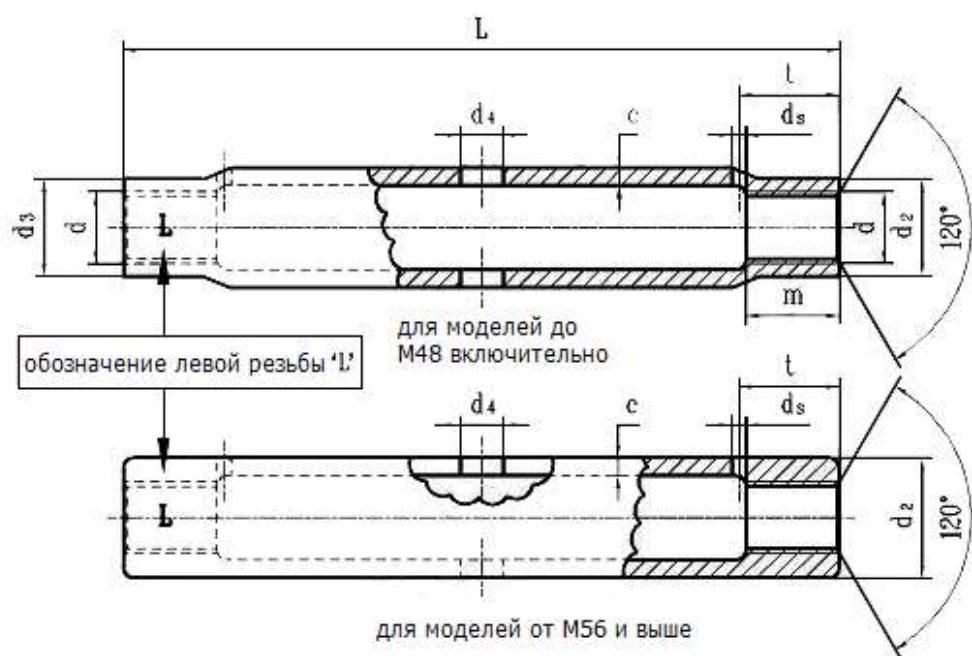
Чертеж талрепа вилка-вилка (закрытого типа)
